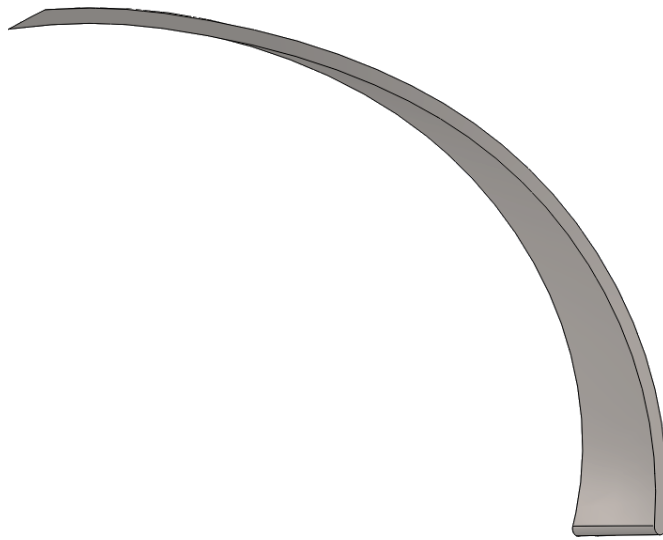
3D модель лопаті робочого колеса в плані
